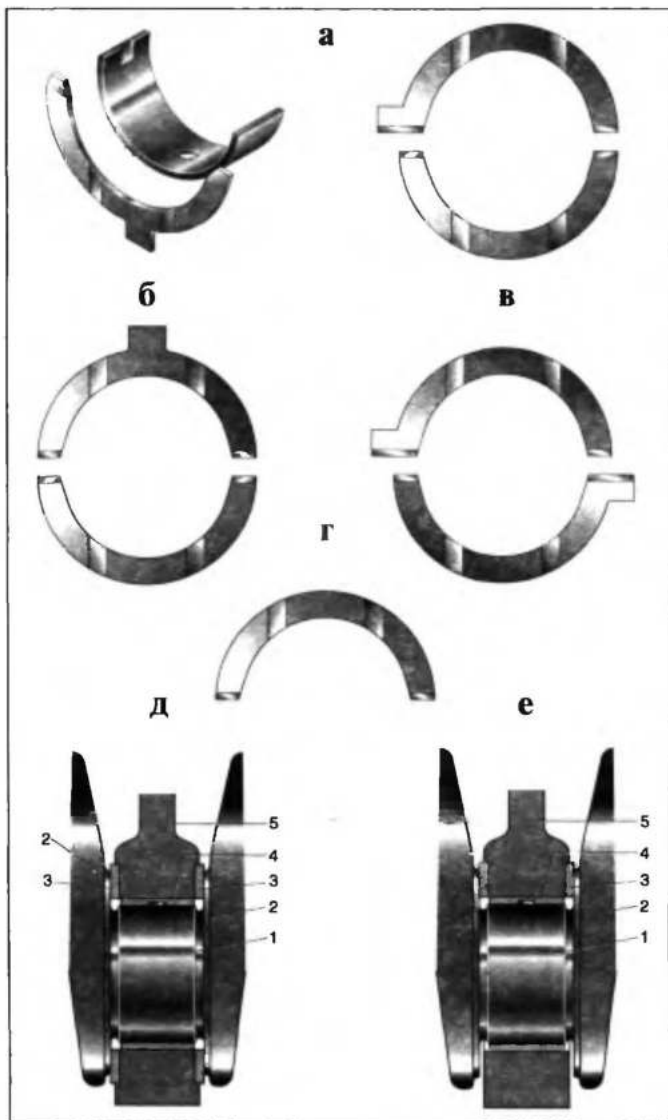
Схема упорного подшипника с полукольцами: а, б, в — пары полуколец, одно из которых имеет фиксирующий выступ; г — простое полукольцо; д — установка двух пар полуколец; е — установка двух простых полуколец; 1 — шейка вала; 2 — щека; 3 — полукольцо; 4 — вкладыш; 5 — опора блока
